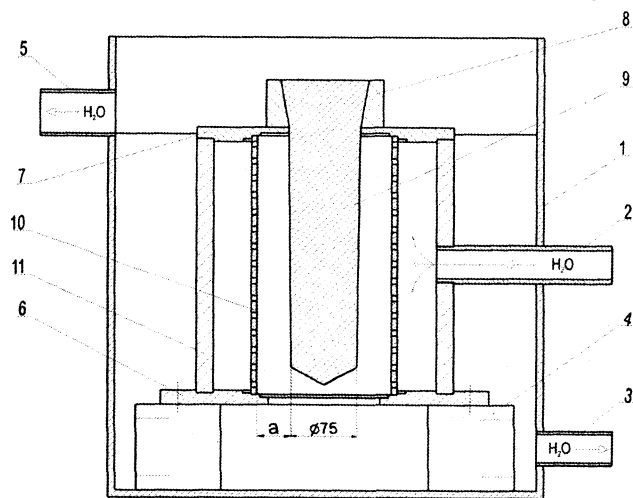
Схема экспериментального устройства затопленно-струйного вторичного охлаждения: 1 – бак; 2 – подводящий патрубок; 3 – отводящий патрубок; 4 – опорный стол; 5 – сливной патрубок; 6 – нижний фланец; 7 – верхний фланец; 8 – захват; 9 – отливка; 10 – экран; 11 – корпус; а – ширина кольцевой щели
